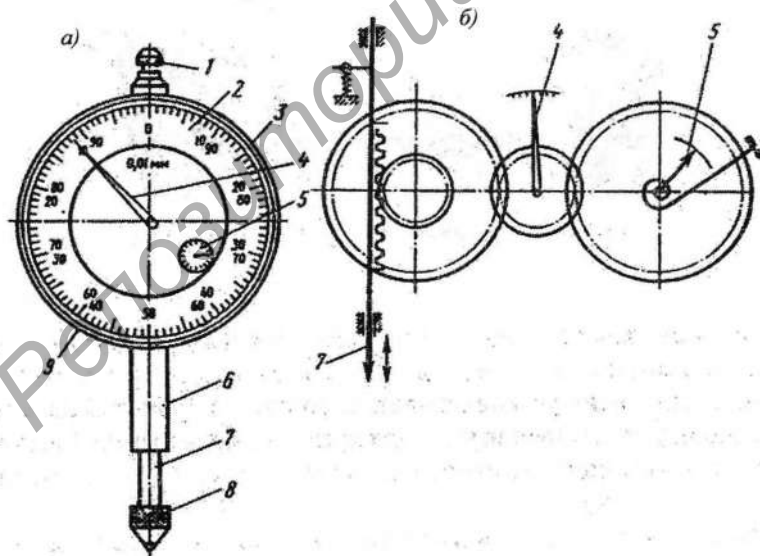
Индикатор часового типа: а — внешний вид, б — принципиальная схема [10, с. 215]
